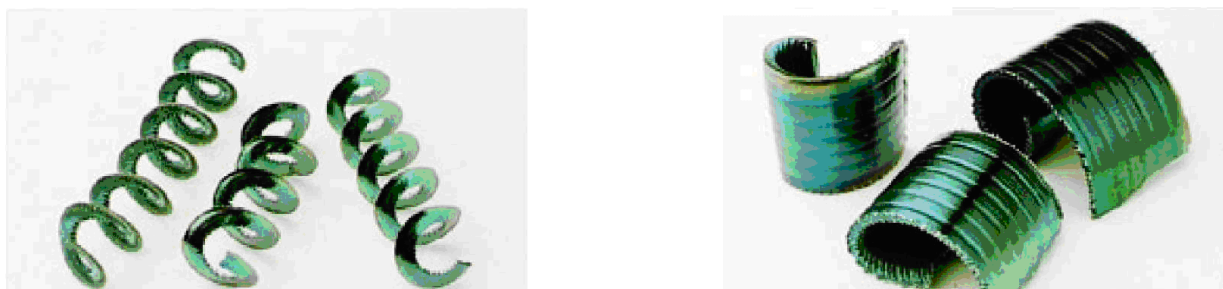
Форма стружки, типичная для чистовой и черновой обработки
